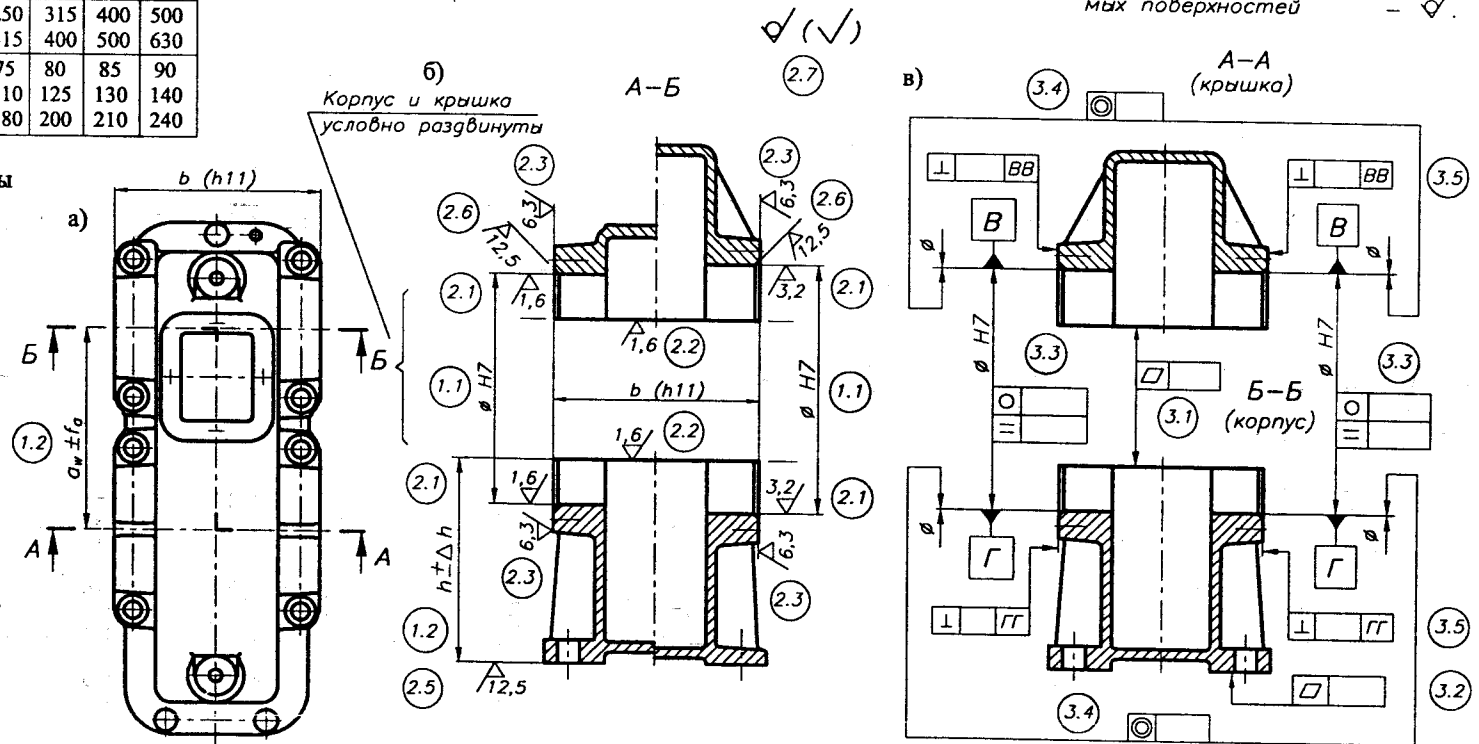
Обозначение на корпусных деталях редукторов:
